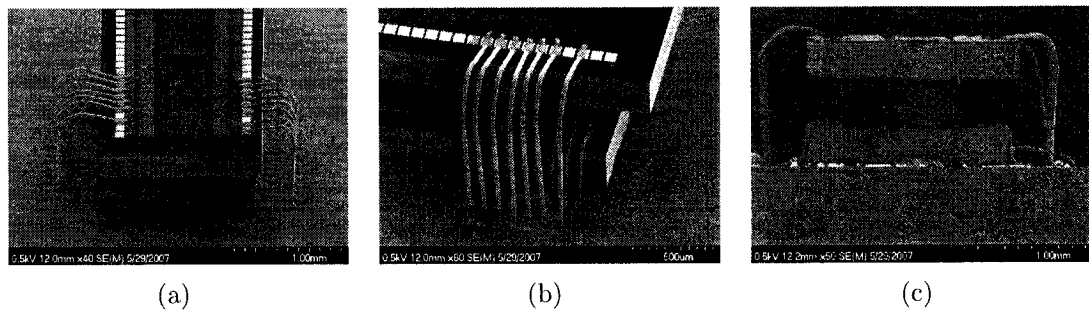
Disposition et connexion du second circuit : a) Vue de haut, b) Vue de côté, c) Vue de face
